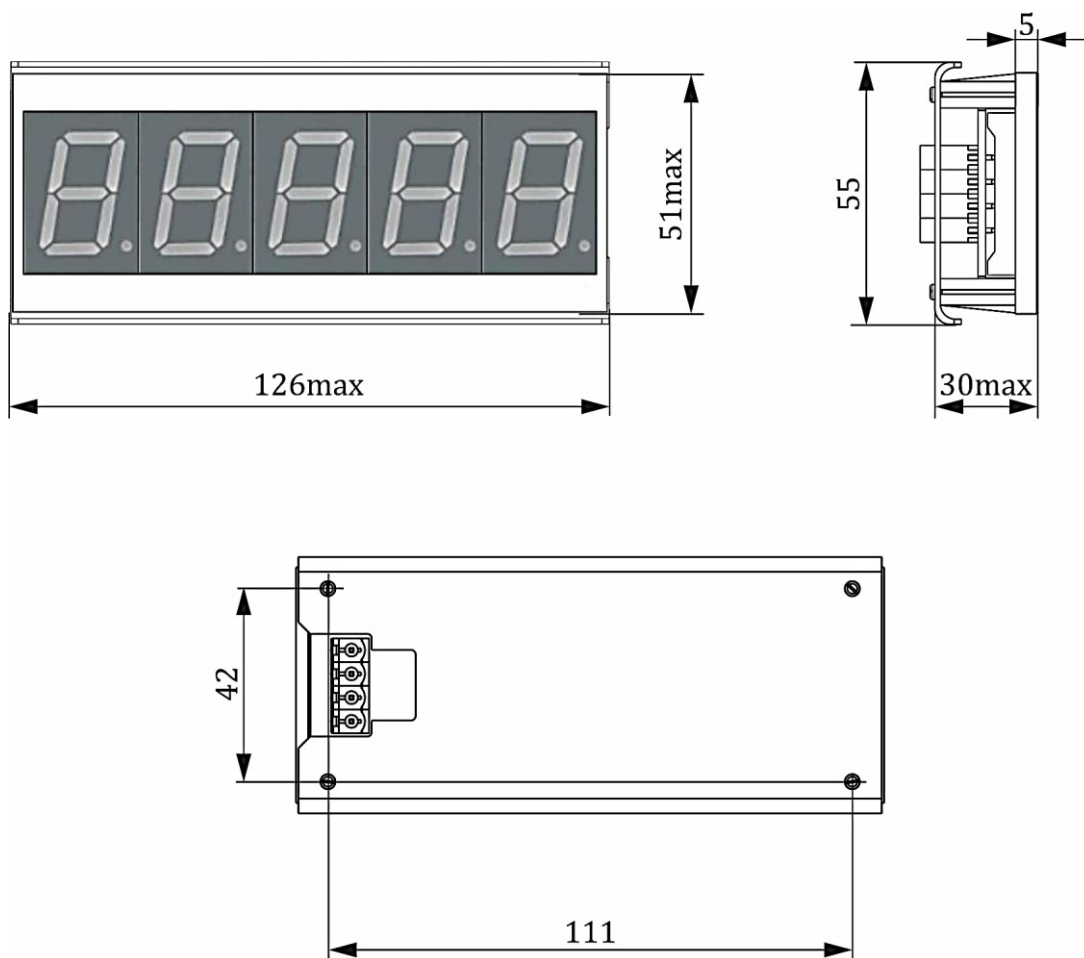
Габаритные и установочные размеры внешнего показывающего устройства E8DU
